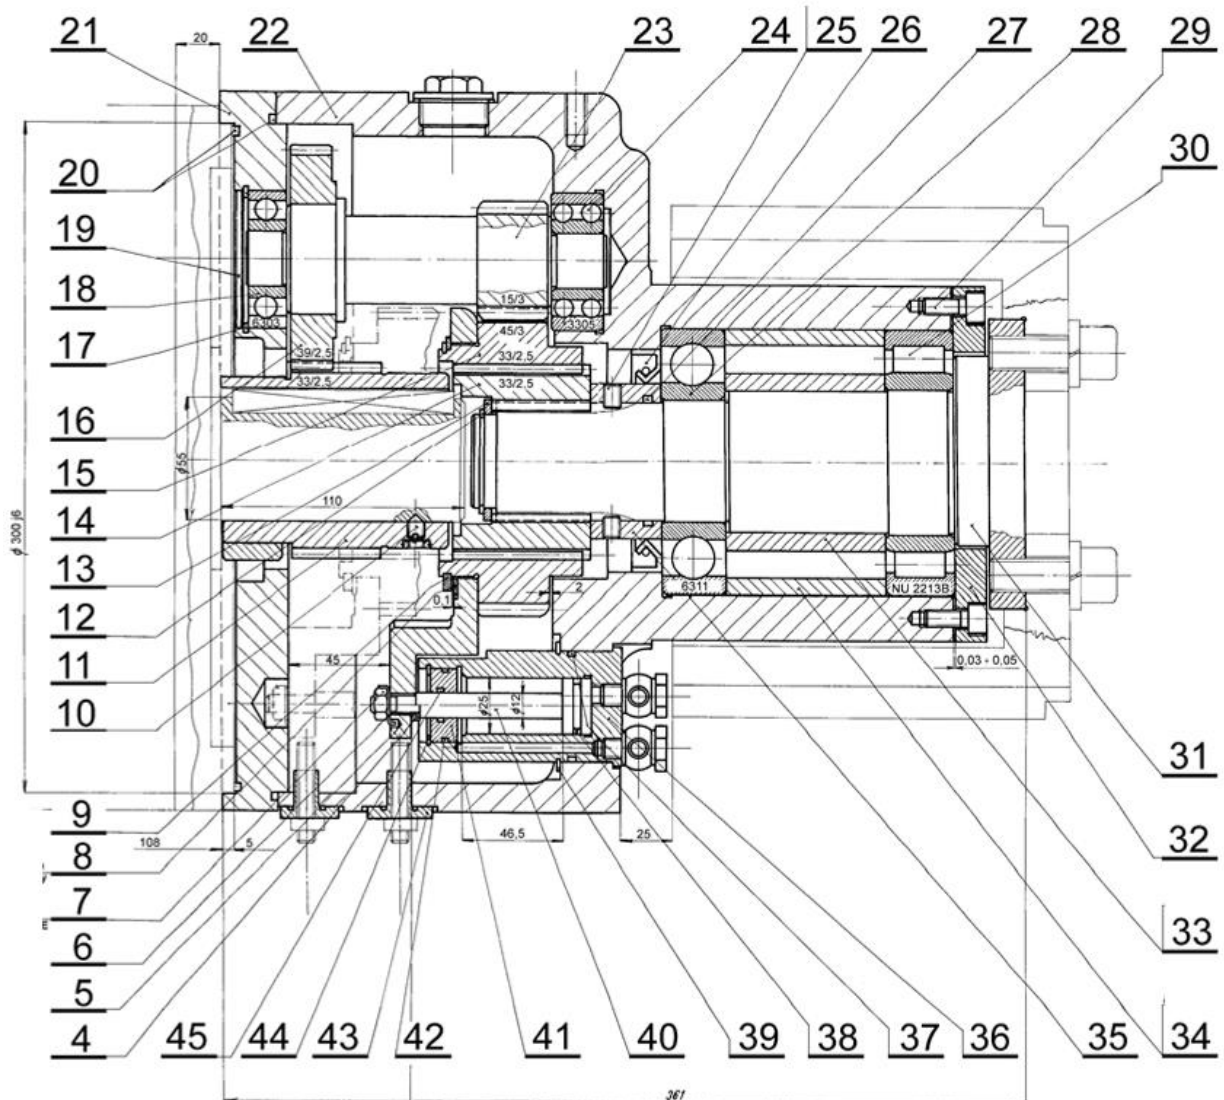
Двоступенева коробка швидкостей токарного верстата з ЧПК мод. SPU 40 CNC
